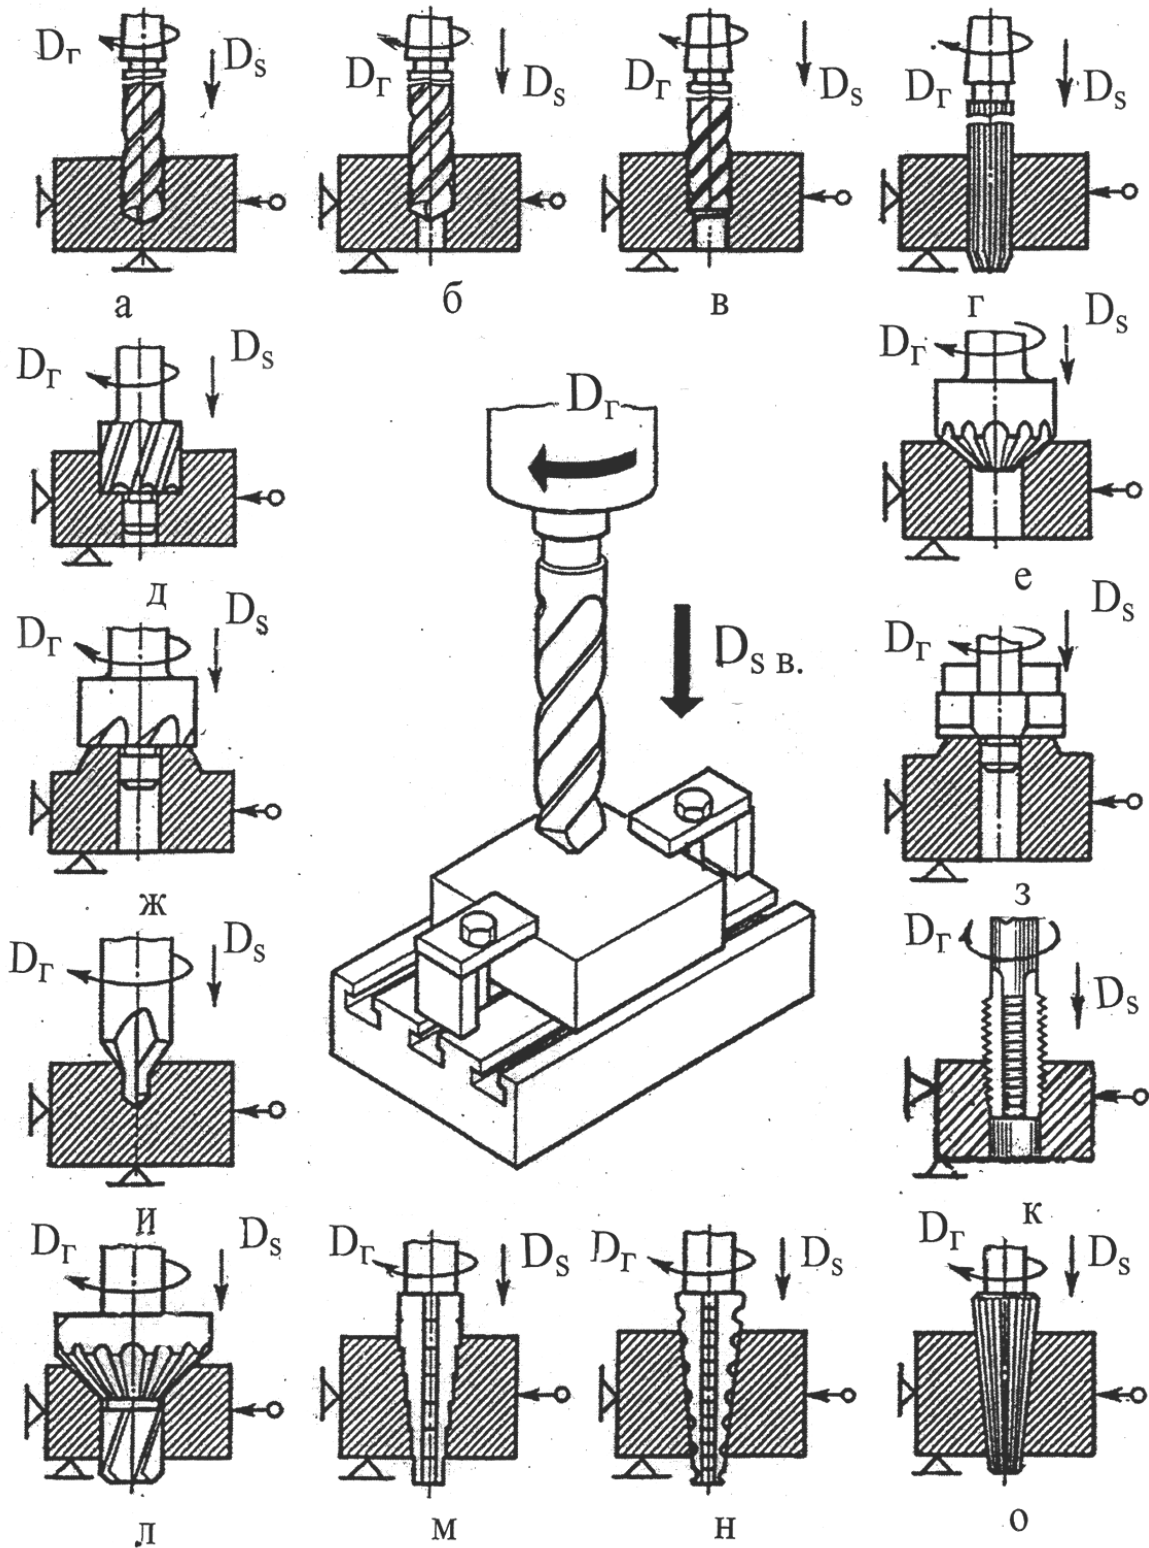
Схемы обработки заготовок на сверлильном станке:
